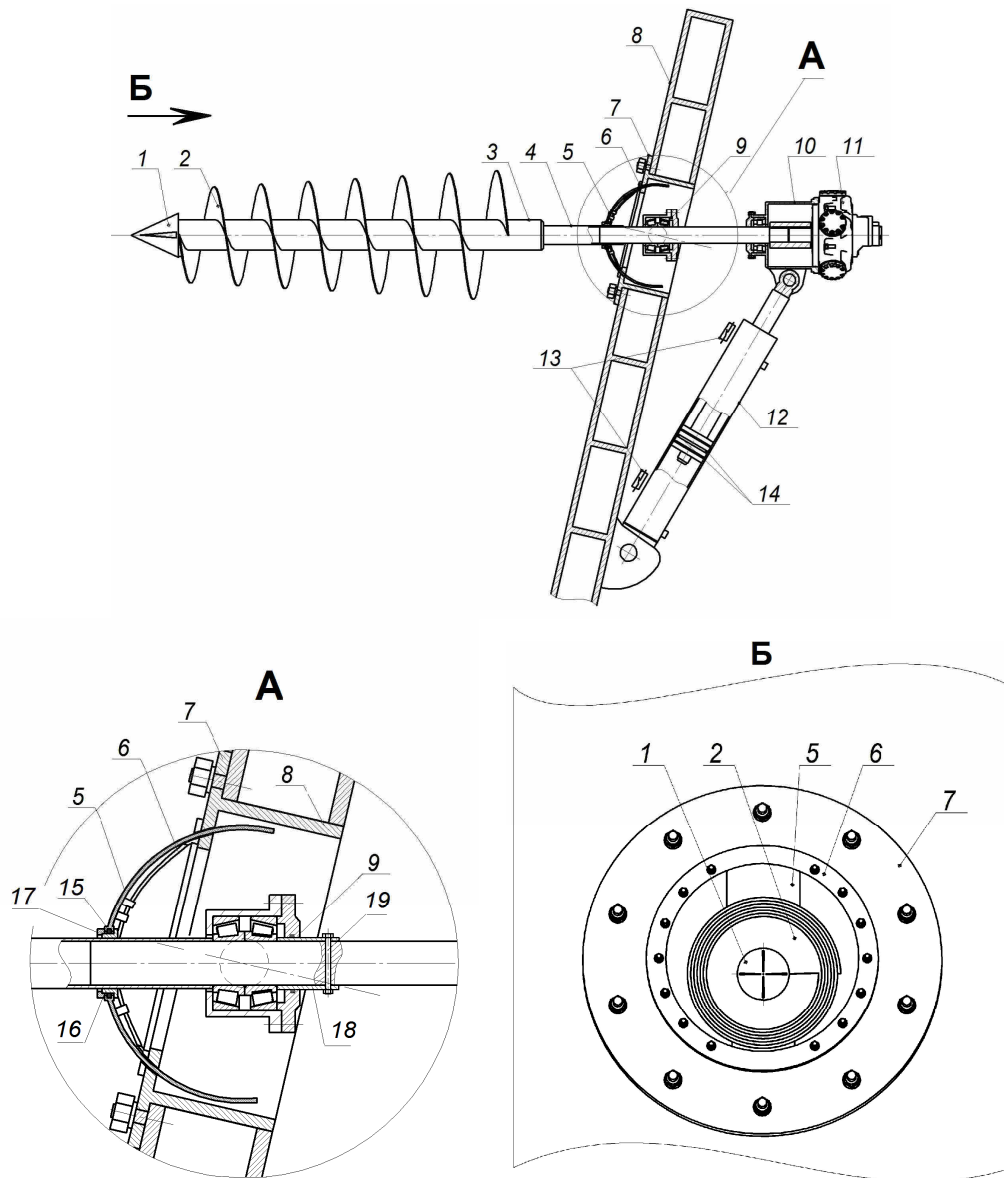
Задня стінка пропонованого скрепера зі шнеками: 1 – наконечник; 2 – шнек; 3 – вал шнека; 4 – циліндричний подовжувач; 5 – захисний кожух; 6 – сферичний корпус; 7 – корпус шнека; 8 – задня стінка скрепера; 9 – поворотна обойма; 10 – рама гідромотора; 11 – привідний гідромотор; 12 – гідроциліндр перекосу шнека; 13 – геркони; 14 – магнітне кільце на поршні гідроциліндра; 15 – ущільнення валу; 16 – втулка; 17 – фіксатор втулки; 18 – стопорна обойма; 19 – болтове з’єднання
